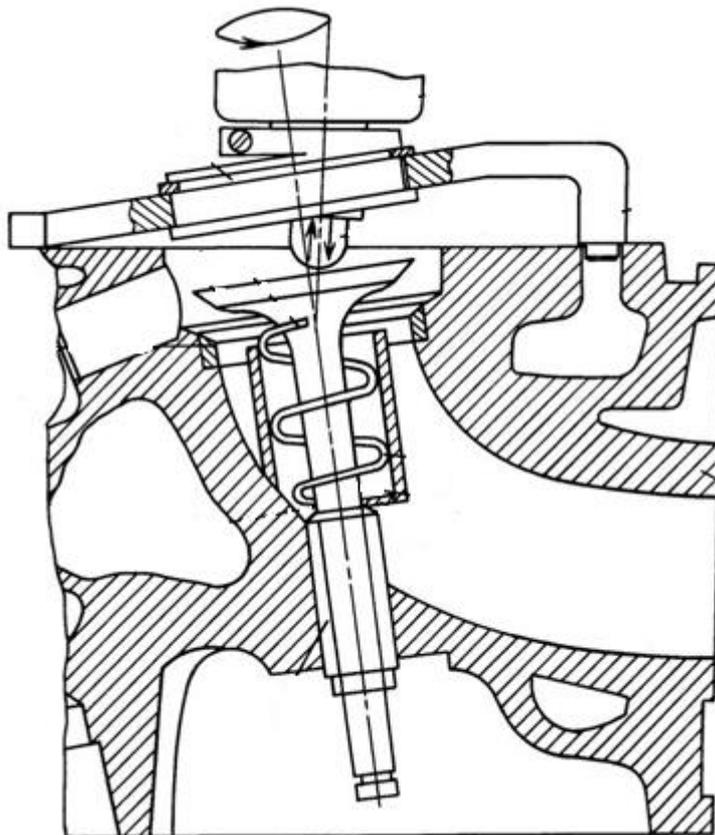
Загальний вигляд схеми роботи клапана
